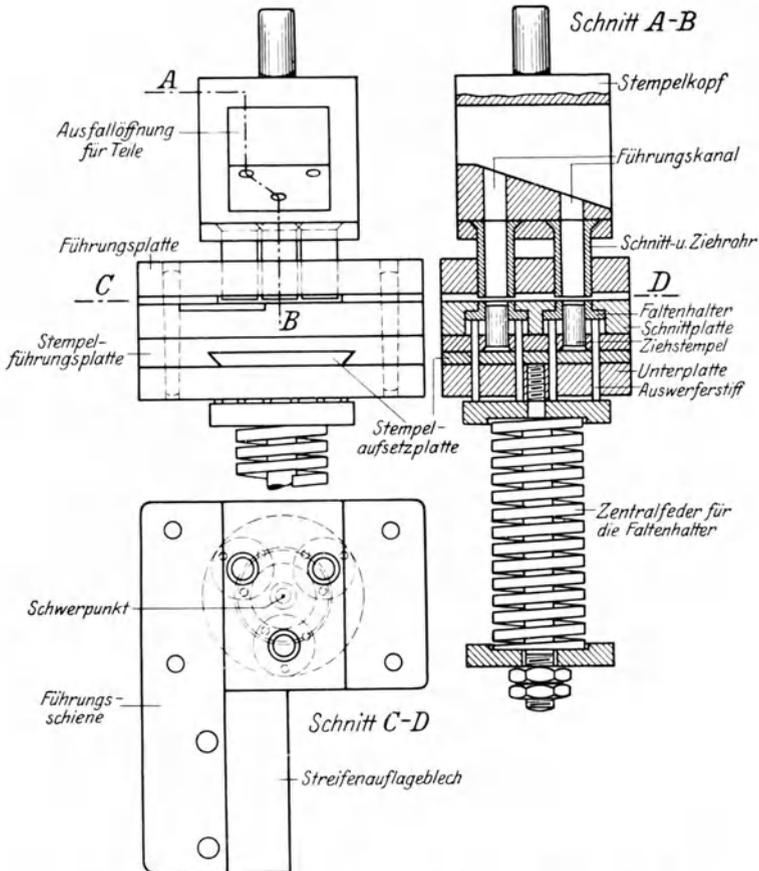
Dreifach wirkendes Schnitt- und Ziehwerkzeug für normale Exzenterpressen.
